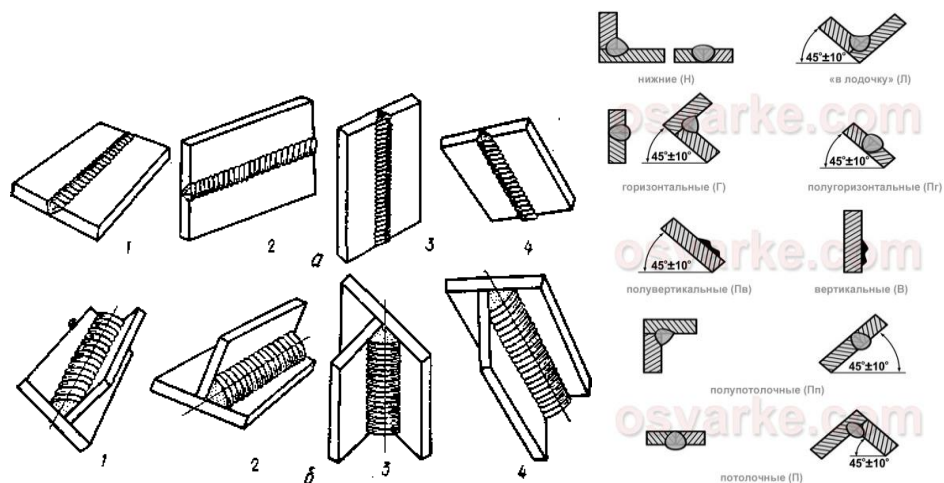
Пространственное положение сварных швов:
